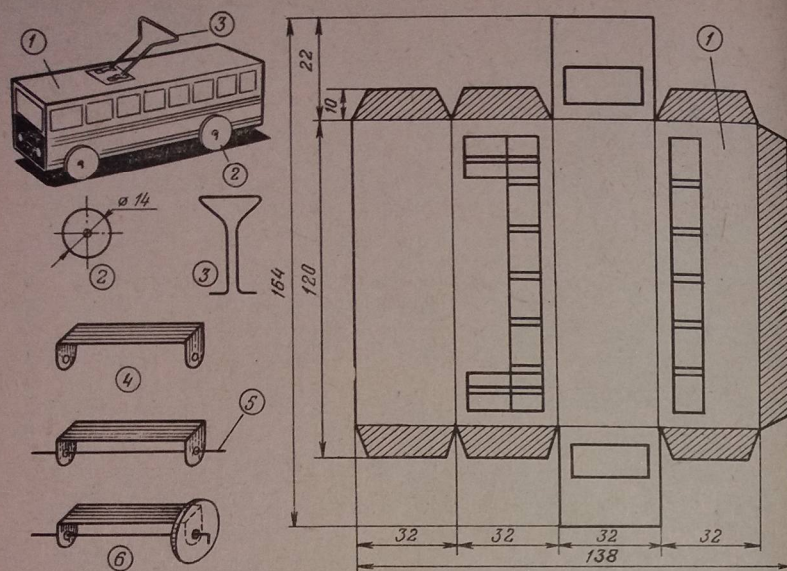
Модель трамвая: 1—развертка кузова; 2—колесо; 3—дуга; 4—скоба; 5—ось; 6—сборка моста ходовой части
